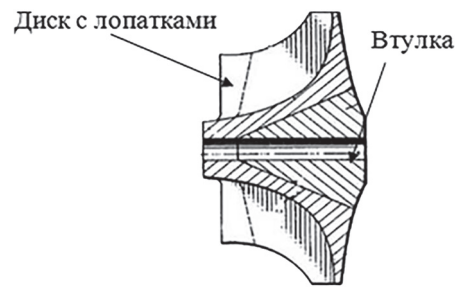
Рабочее колесо компрессора с втулкой из материала повышенной прочности
